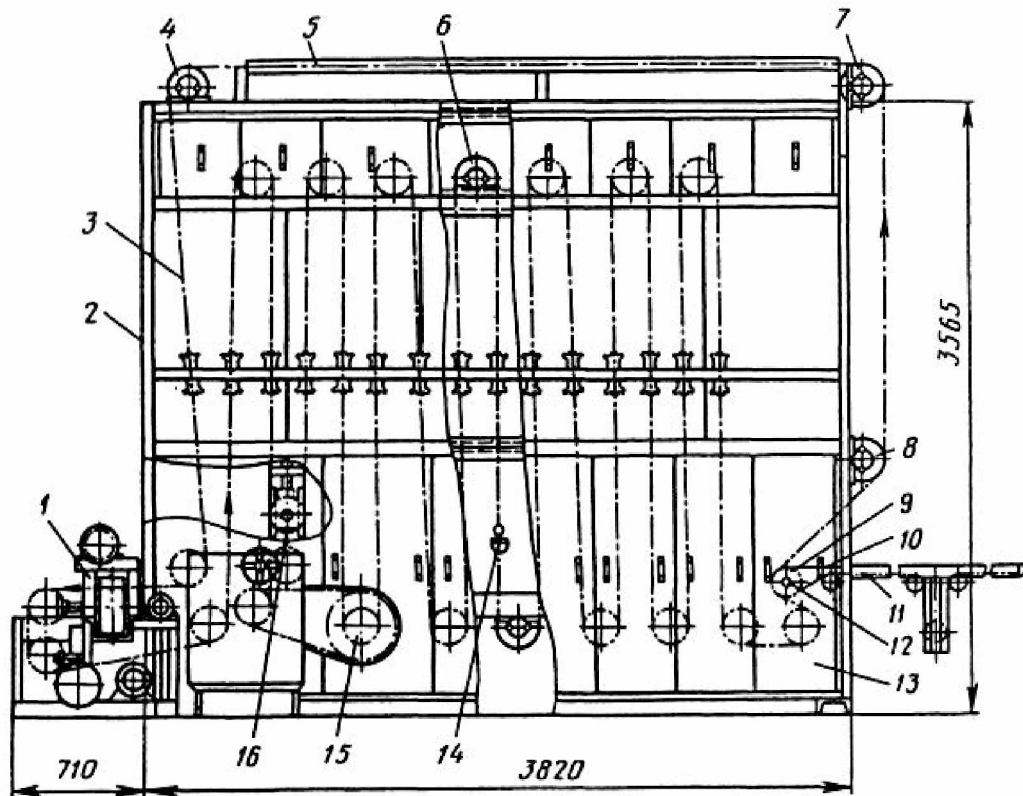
Шафа вистою РШВ: 1 - зона завантаження пустих кошиків; 2 – каркас; 3 – ланцюговий транспортер; 4, 7, 8 – зірочки; 5 - зворотня гілка конвеєра; 6 - пара зірочок; 9 - спеціальний транспортер; 10 - стрічковий транспортер; 11 – напрямна; 12 - барабан транспортера; 13 - з’ємне огороження; 14 - кошика; 15 – зірочки; 16 - натяжна станція.
